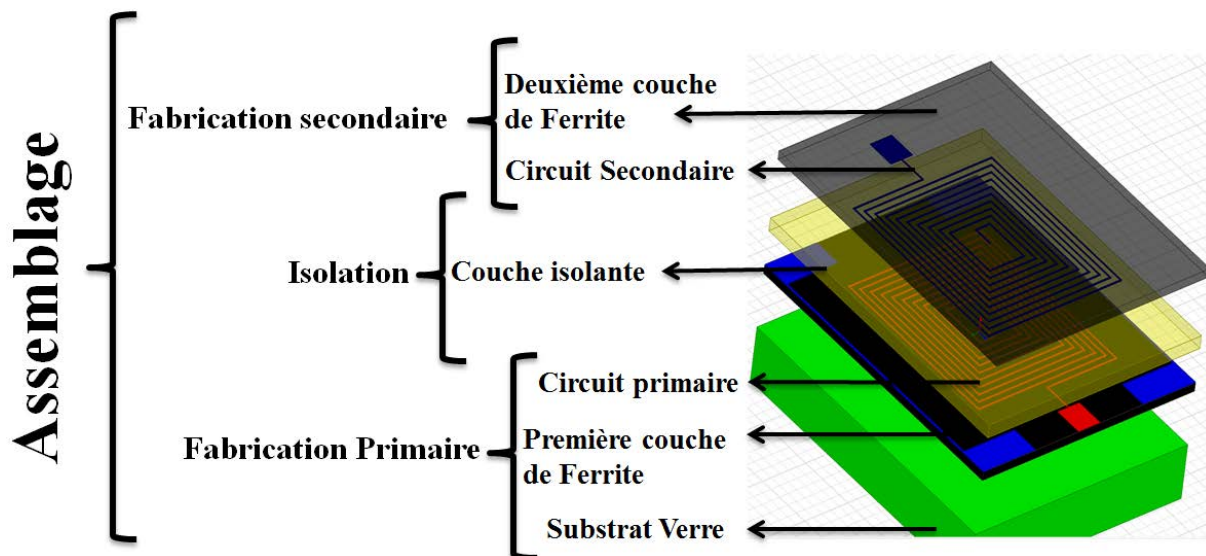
Etapes de fabrication du transformateur Face-To-Face
